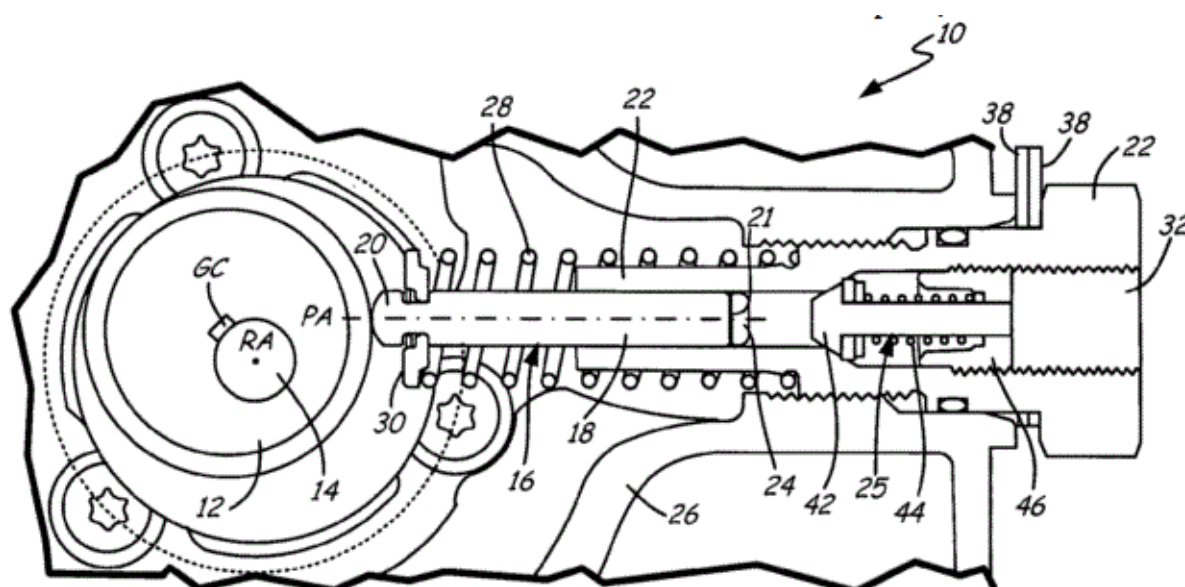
Ескіз до патенту 2564155 «Зміщений кулачок для поршневого насоса»: 10-вузол насоса; 12-кулачок; 14-привідний вал; 16-поршень; 18-прямий вал; 20-ролиу; 22-циліндр; 24-впускний отвір; 25-клапан; 26-основа-; 28-пружина; 30-опора; 32-випускний отвір; 36-кільце; 38-затискач; 42-пробка; 44-пружина; 46-опора.
